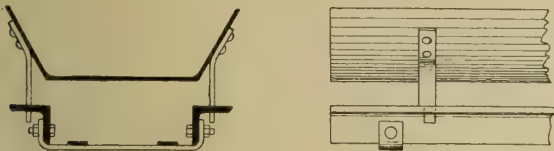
Querschnitt und Ansicht der Rinne des Blackett-Conveyors.
